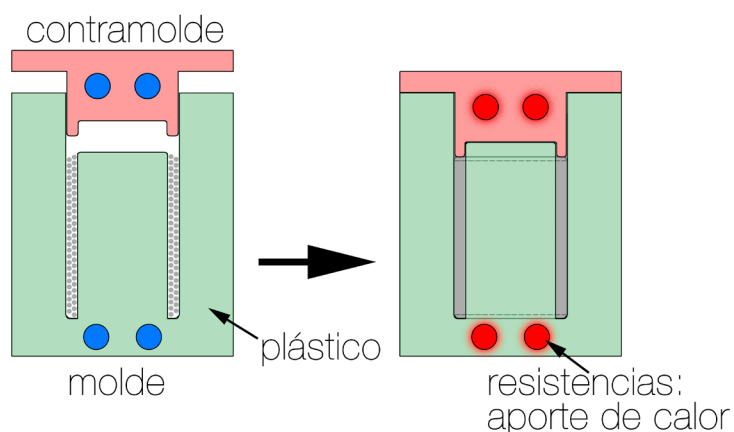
moldeo por compresión pieza "4.4.2.- Goma antivibración"
